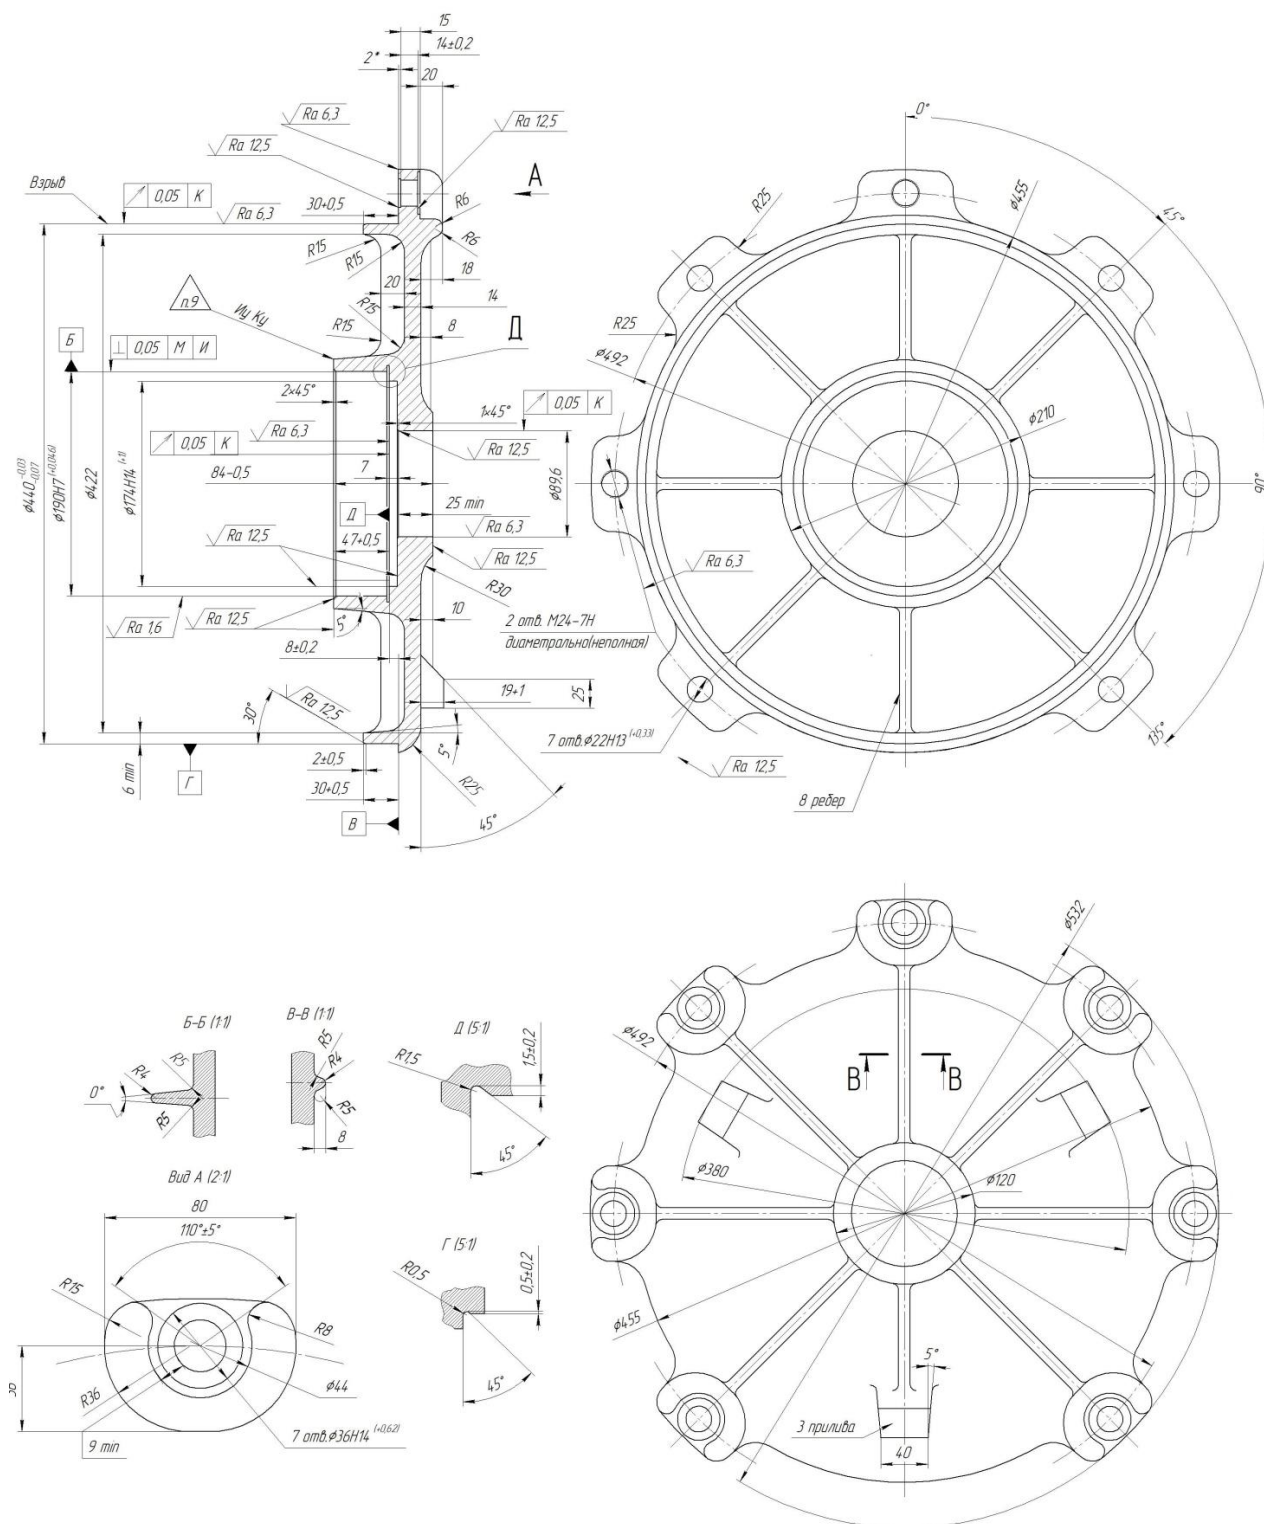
Чертеж подшипникового щита взрывозащищенного электродвигателя модели ABP250
